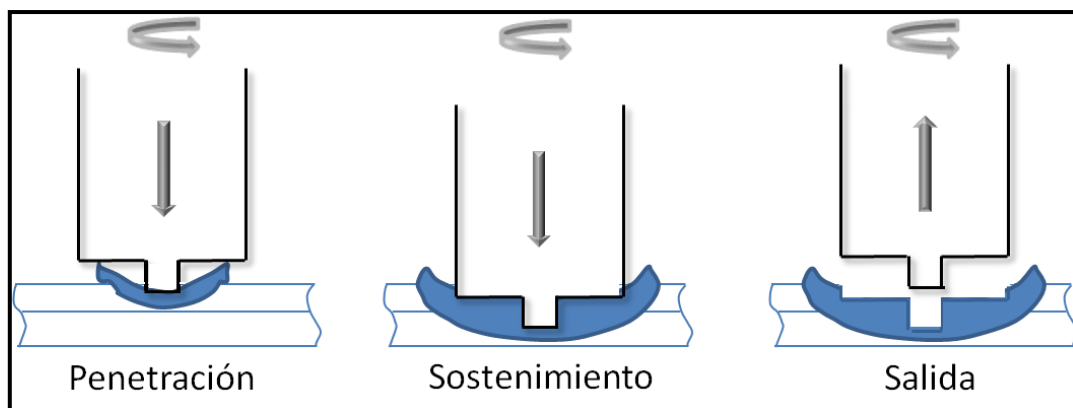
Esquema de proceso de soldadura FSSW
